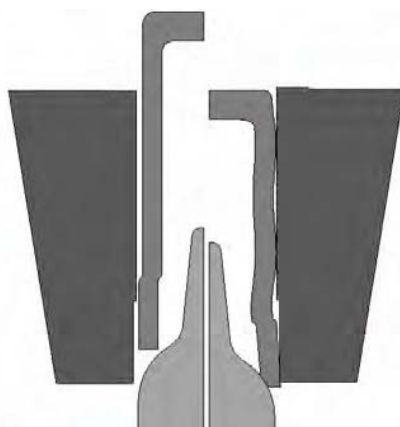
Запрессовка колпачка со ступенчатым изменением внутреннего и наружного диаметров
